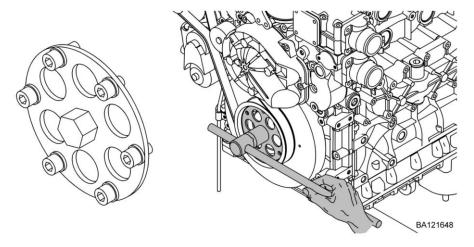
Dispositivo de giro - Montaje de la polea de transmisión del cigüeñal, herramienta especial núm. 30a
